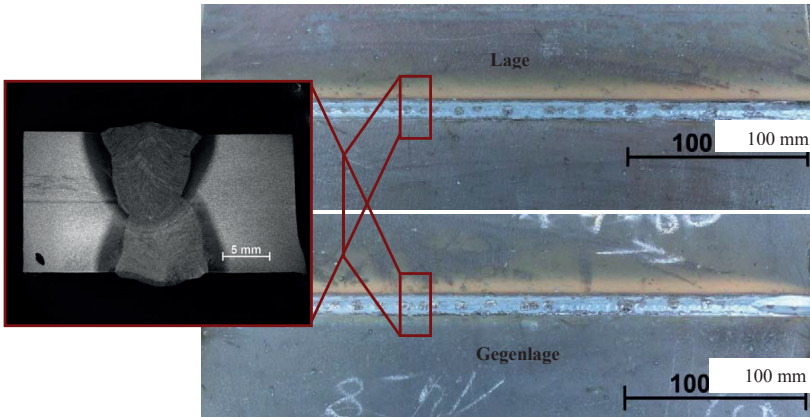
Zweiseitig ausgeführte Schweißnaht
